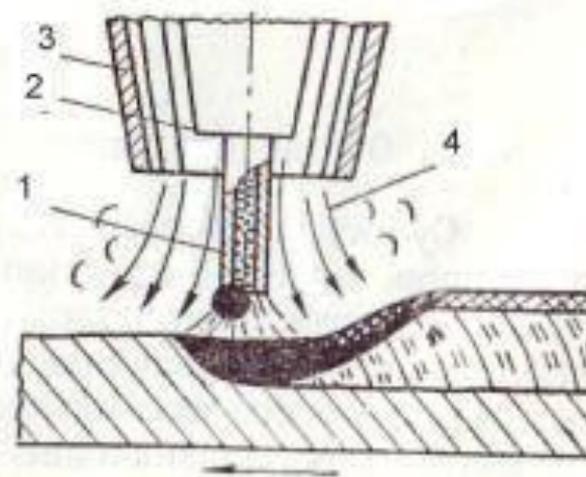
Схема процесса сварки порошковой проволокой в углекислом газе
